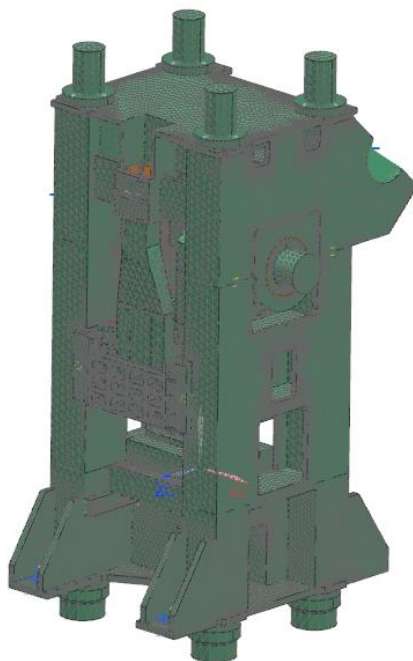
Horní příčnick výchozí konstrukce - žebra
